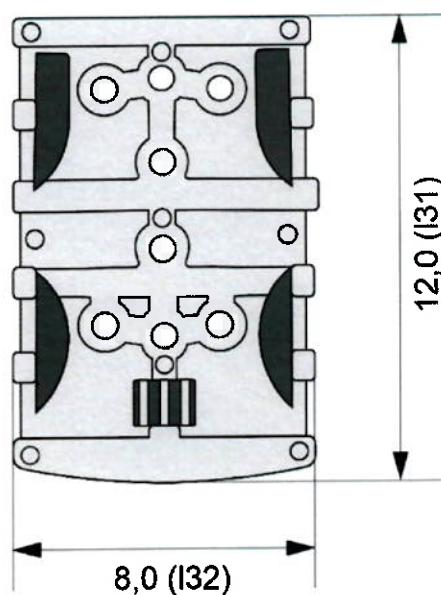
Detalhes do coldre tático todo montado junto com a plataforma de perna
